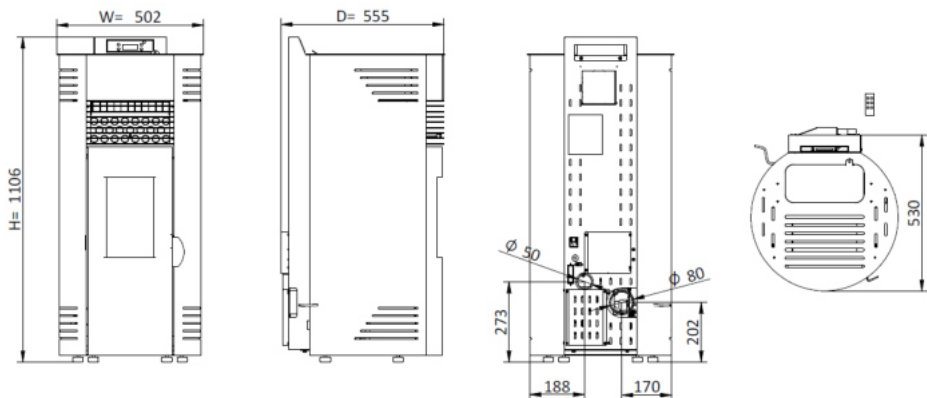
B – Dimensiones de la estufa de *pellets* Indie 8 kW
